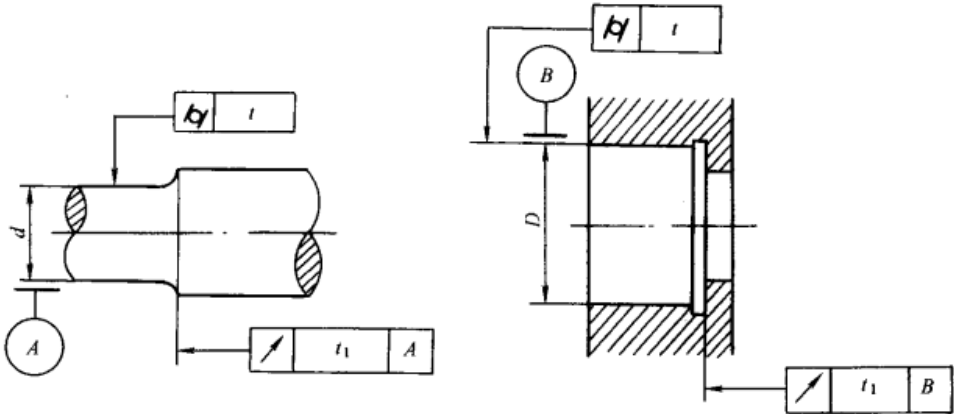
轴与外壳孔配合表面及端面的形位公差
